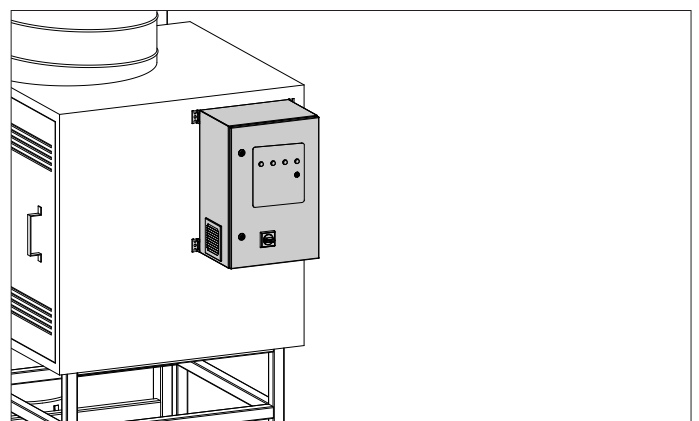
Montage du Panel sur le boîtier de ventilateur
